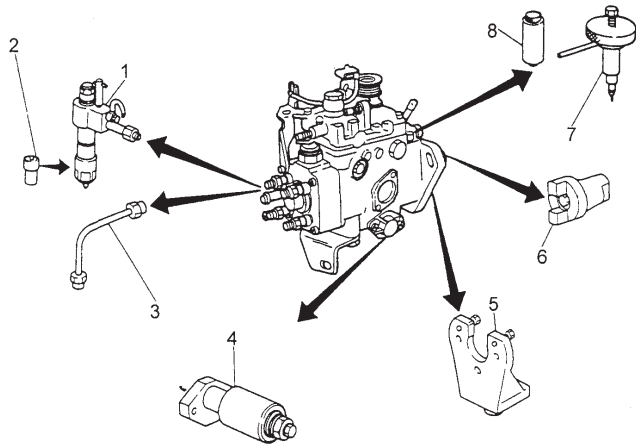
Приспособления для испытаний ТНВД VE: 1 - эталонная форсунка; 2 - корпус распылителя; 3 - трубка ЛВД; 4 - приспособление для измерения хода поршня автомата опережения впрыскивания; 5 - кронштейн для установки насоса на топливном стенде; 6 - муфта привода ТНВД на стенде; 7 и 8 - приспособления для разборки и сборки регулятора низкого давления.
